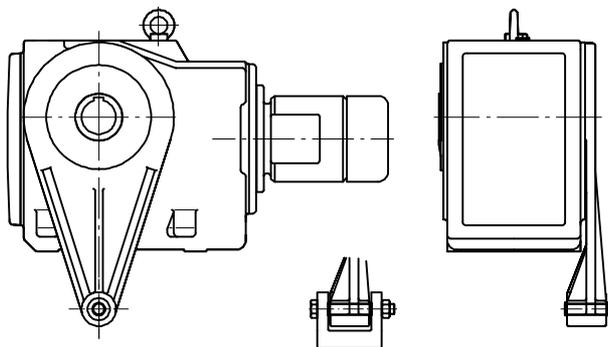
Крепление упора против проворачивания на конических и червячных редукторах
